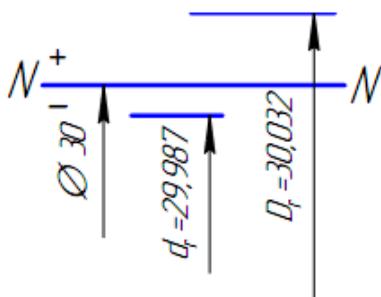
Схема расположения номинального и действительных размеров (отклонений) соединения
